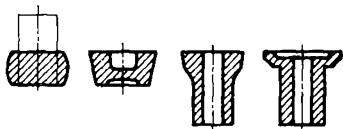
Схема четырехпереходной (считая осадку) штамповки поковки с наметкой и прошивкой сквозной полости
